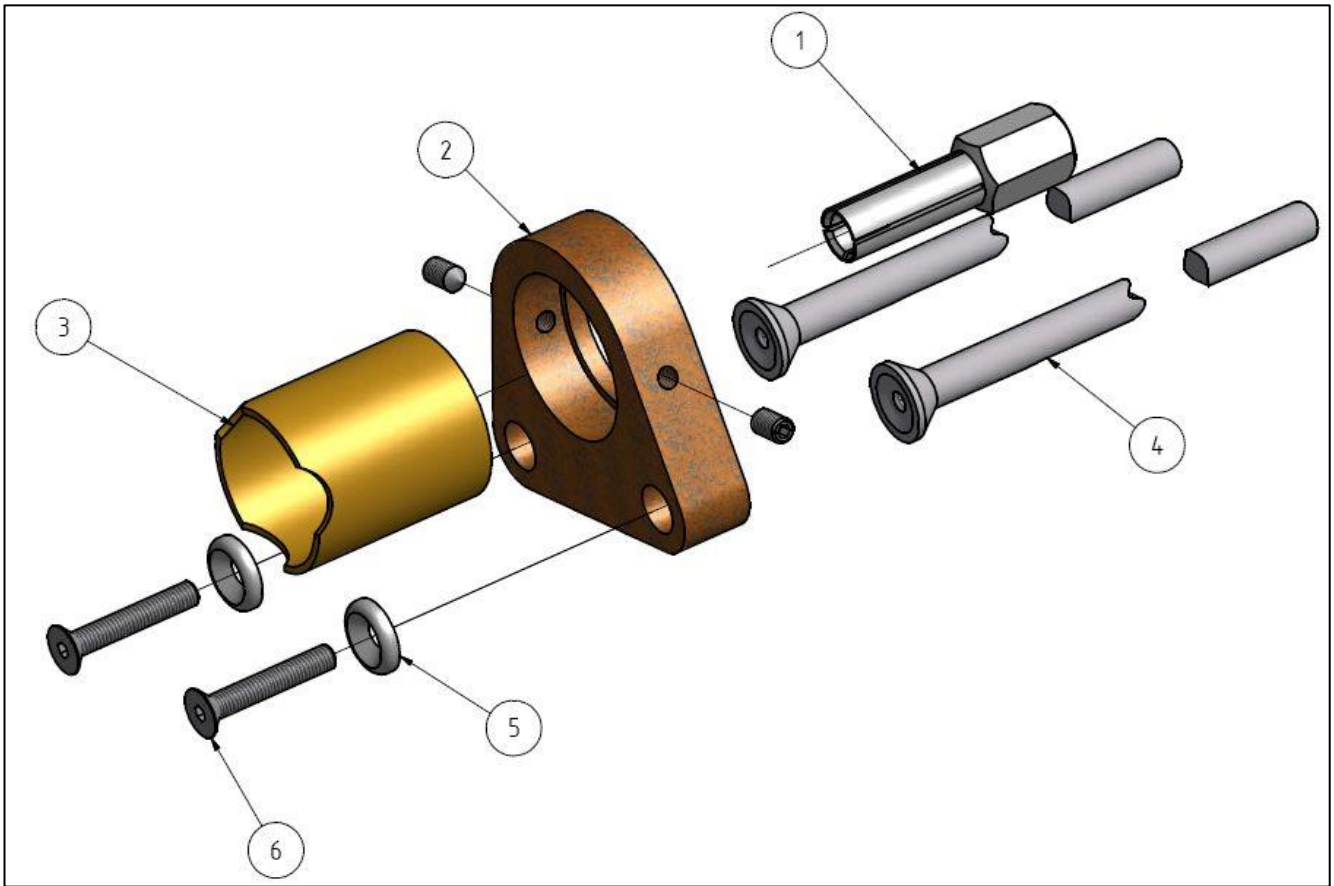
Stützeinrichtung zum Kurzzeitbolzenschweißen ohne Schutzgas
